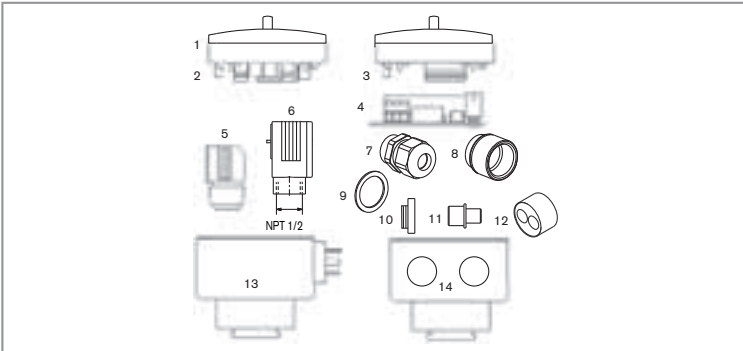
Ersatzteil-Explosionszeichnung für den 8035
